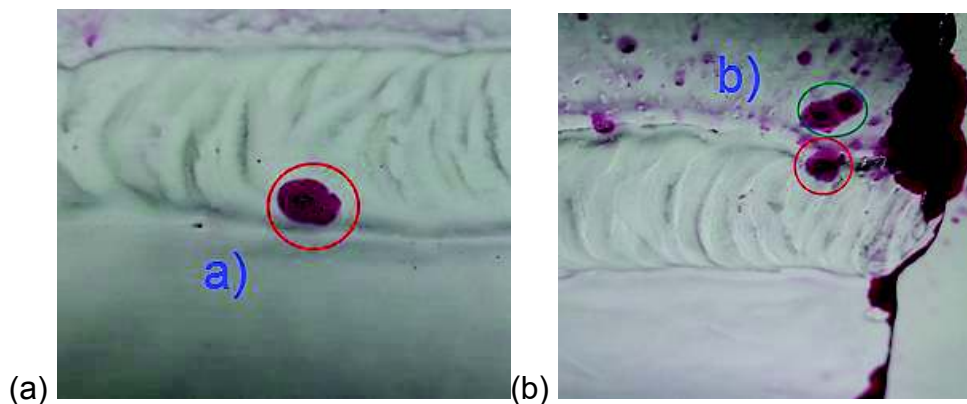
(a), (b) Ampliación de los defectos del cordón de soldadura en las placas
